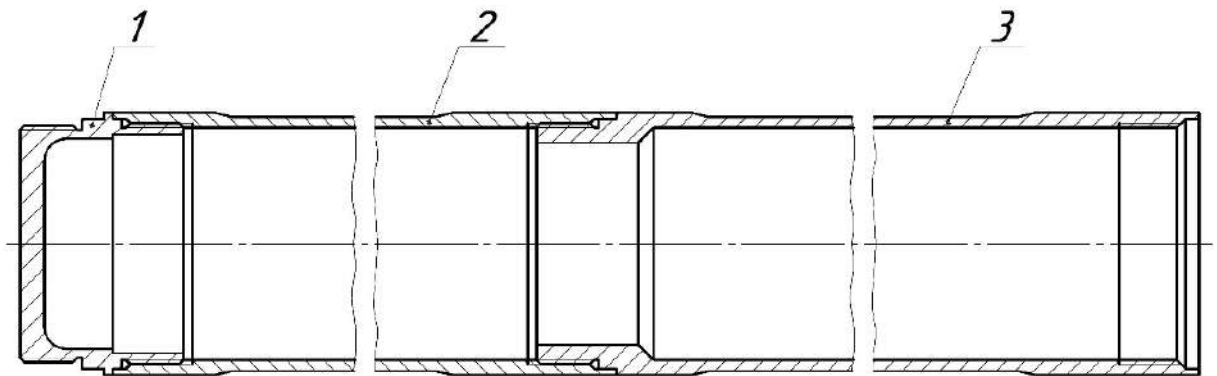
Корпус ракетного двигателя (тип №2):
